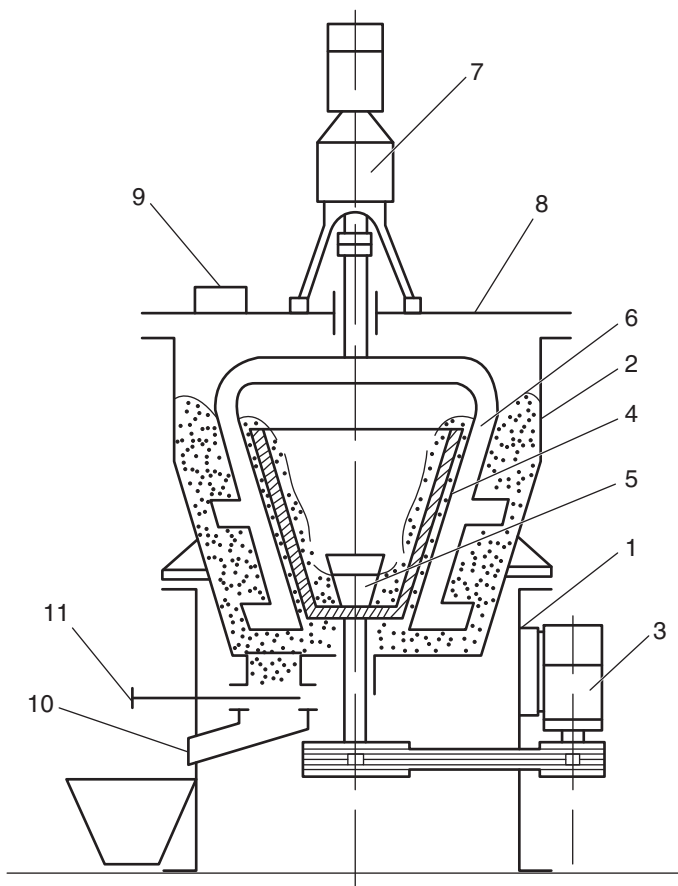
Схема смесителя центробежного действия: 1 — корпус; 2 — емкость; 3 — двигатель; 4 — полый конус; 5 — окна; 6 — мешалка; 7 — привод; 8 — крышка; 9 — люк; 10 — лоток; 11 — шибер
